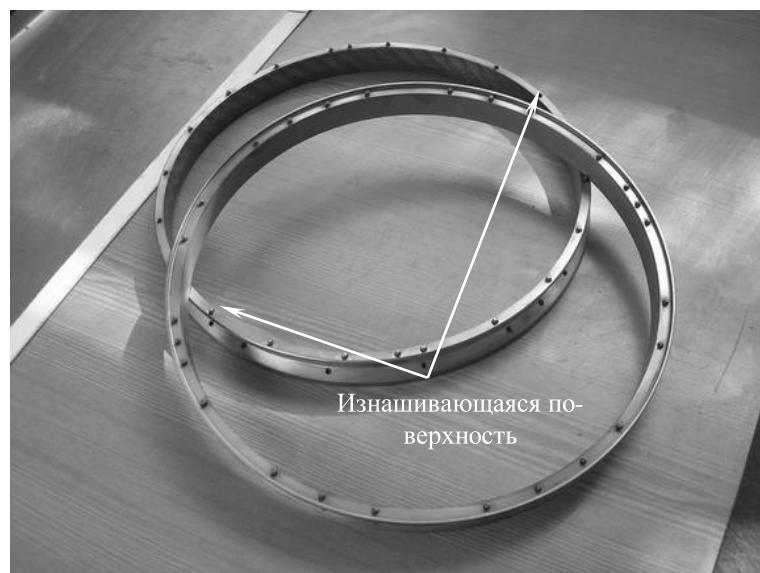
Кольца рабочих колес компрессора вертолетного двигателя
